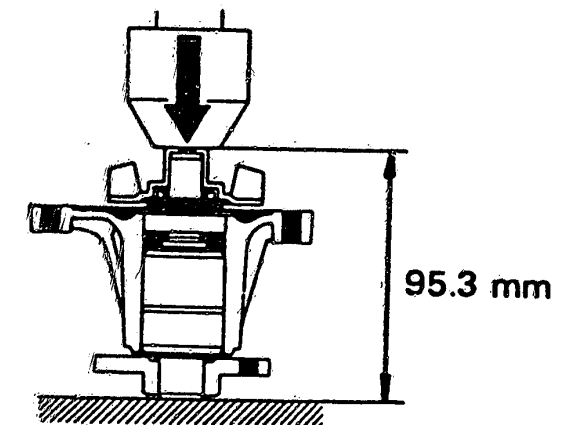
Der Rotor ist soweit einzupressen, dass die Länge der Wasserpumpe 95,3mm beträgt.
